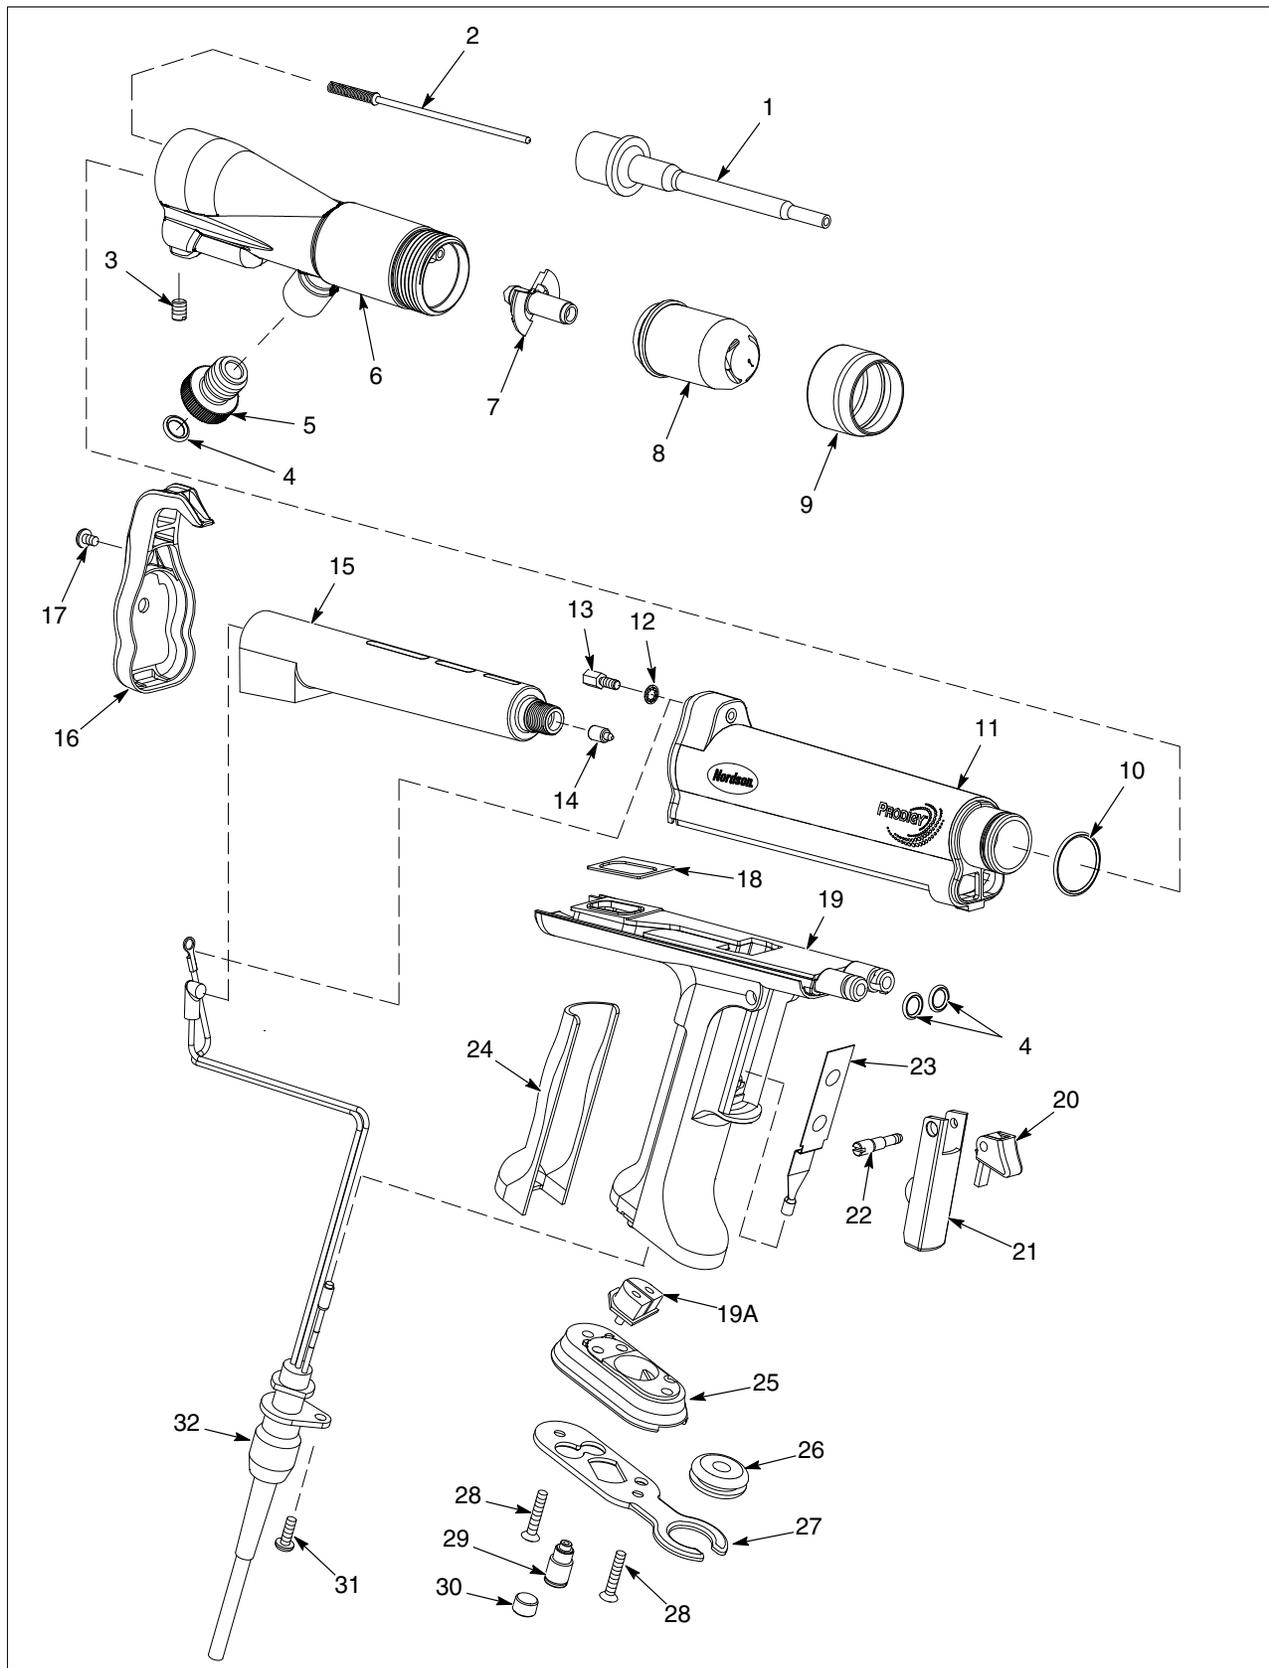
Ilustração explodida das peças da pistola manual de pintura Prodigy
